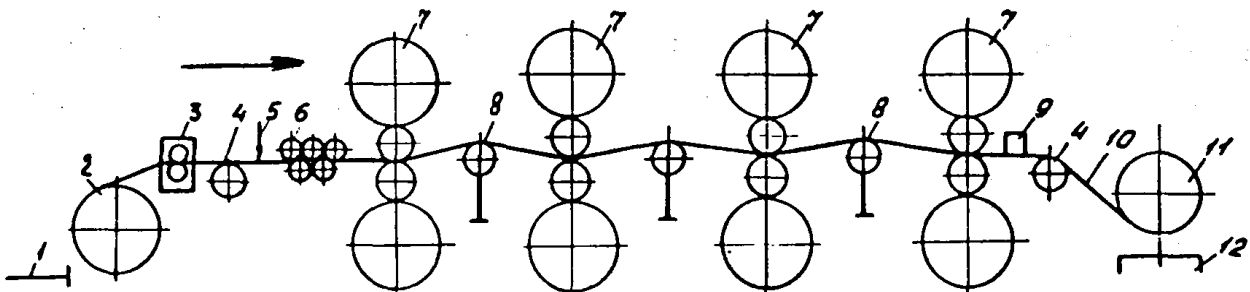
Схема розташування устаткування неперервного чотирьохкільцевого стана порулонної холодної прокатки : 1 - приймальний транспортер; 2 - розмотувач; 3 - відгинач кінців рулонів; 4 - обвідною ролик; 5 - індикатор шва; 6 - роликівий натягувач ; 7 -чотирьохвалкові кліти; 8 - ролик тензометричного пристрою; 9 - товщиномір; 10 - готова штаба; 11 - моталка; 12 - прибиральний транспортер
